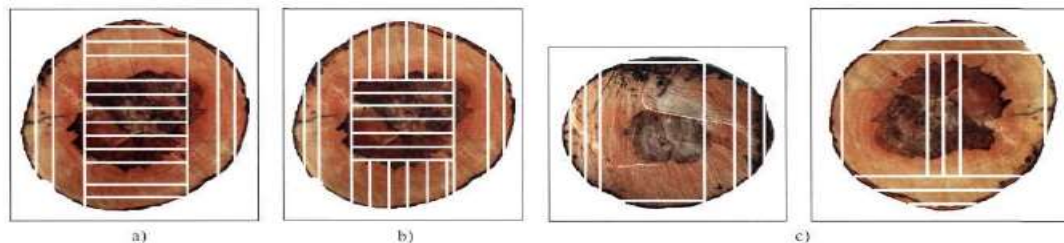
Primjer piljenja bukavih trupaca kružnim načinom piljenja
